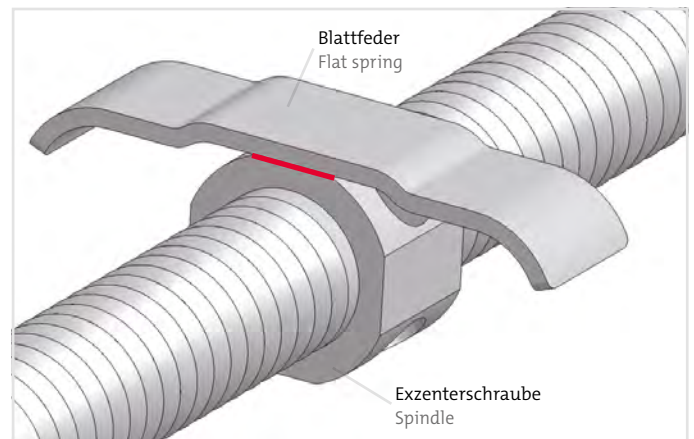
Anfangs- und Endposition, bereit zur weiteren Aktivierung (Blattfeder in Ruheposition). Die Feder übt Druck auf die Exzentrerschraube aus. Auf der ebenen Fläche der Exzentrerschraube rastet die Feder ein und hält diese in einer Position, die für die weitere Aktivierung ideal ist.
